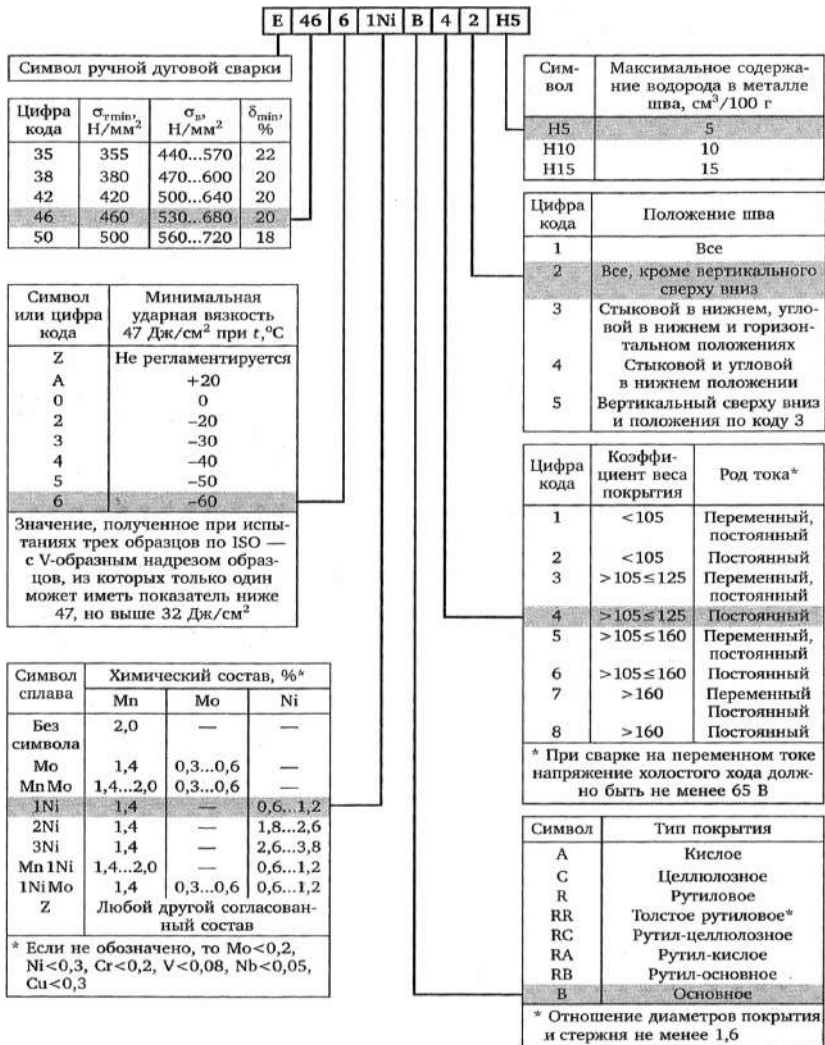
Условные обозначения покрытых электродов для ручной дуговой сварки конструкционных термически улучшенных сталей с мелкозернистой структурой согласно европейскому стандарту EN-499
